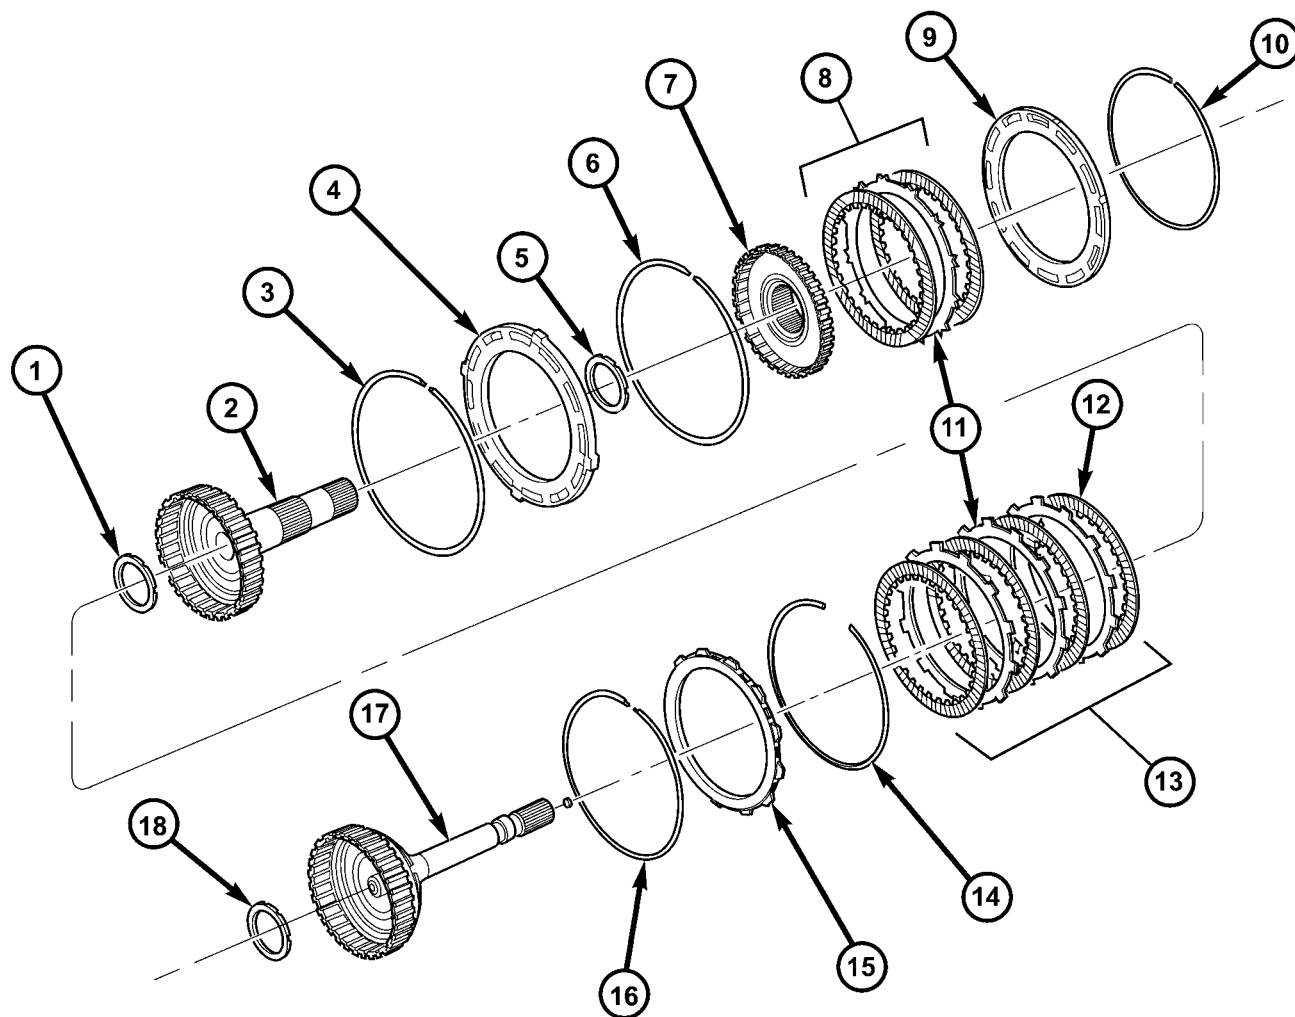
Conjunto de embrague de impulsión - Parte 2
